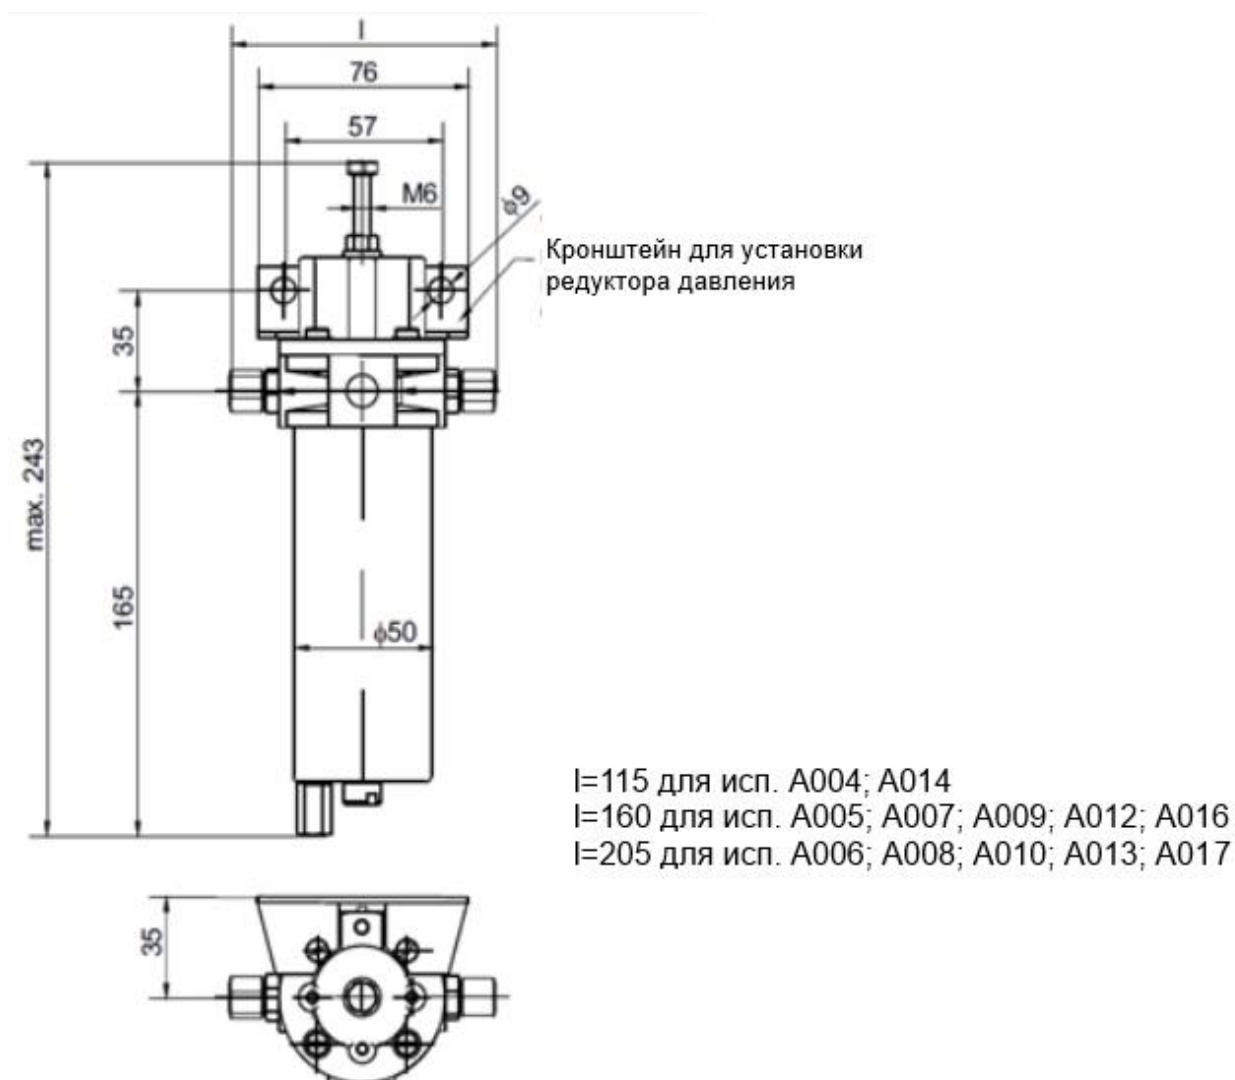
Габаритные размеры редуктора с фильтром тип R110
